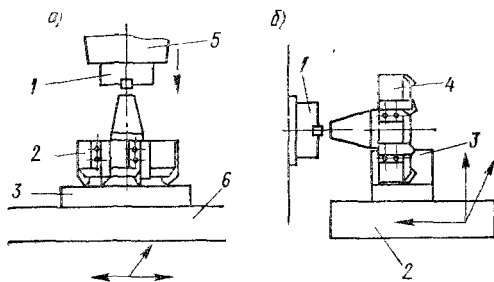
Способы установки на станке крупных и тяжелых фрез
